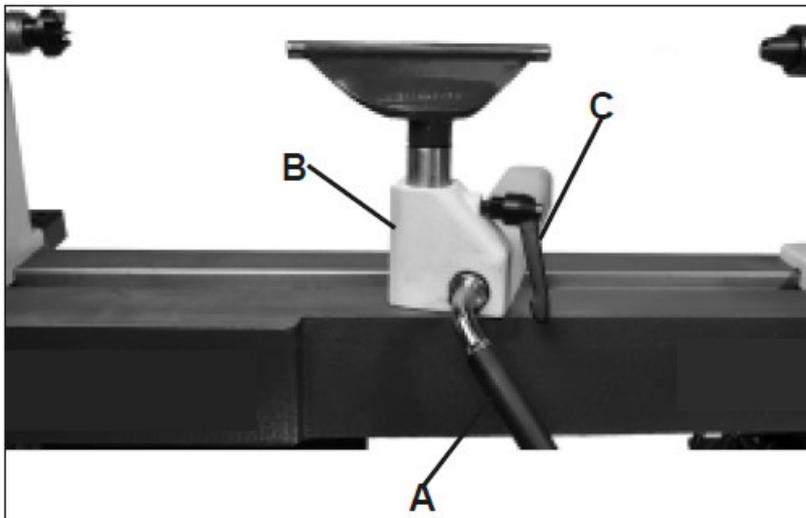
Bedienelemente an der Werkzeugauflage
